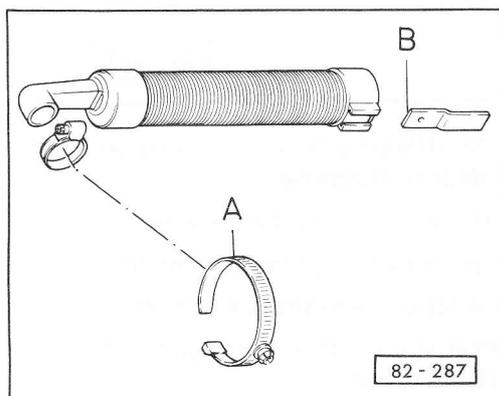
Soufflante d'air de combustion – V6: réglage
